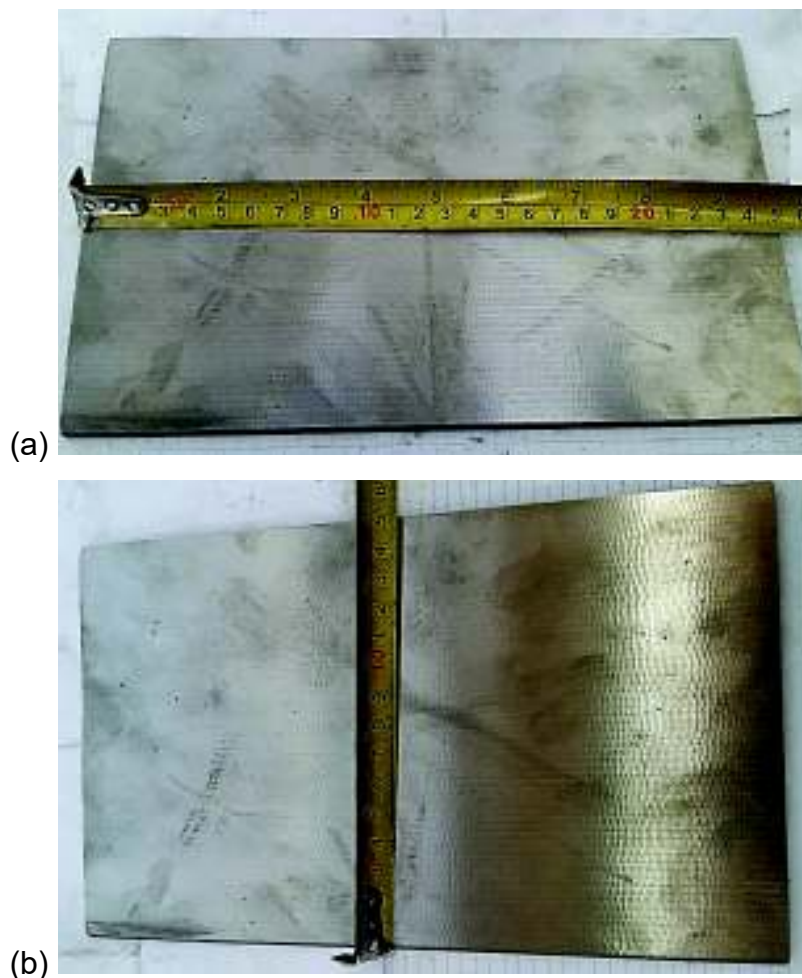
Dimensiones de la placa para ensayo de soldabilidad
